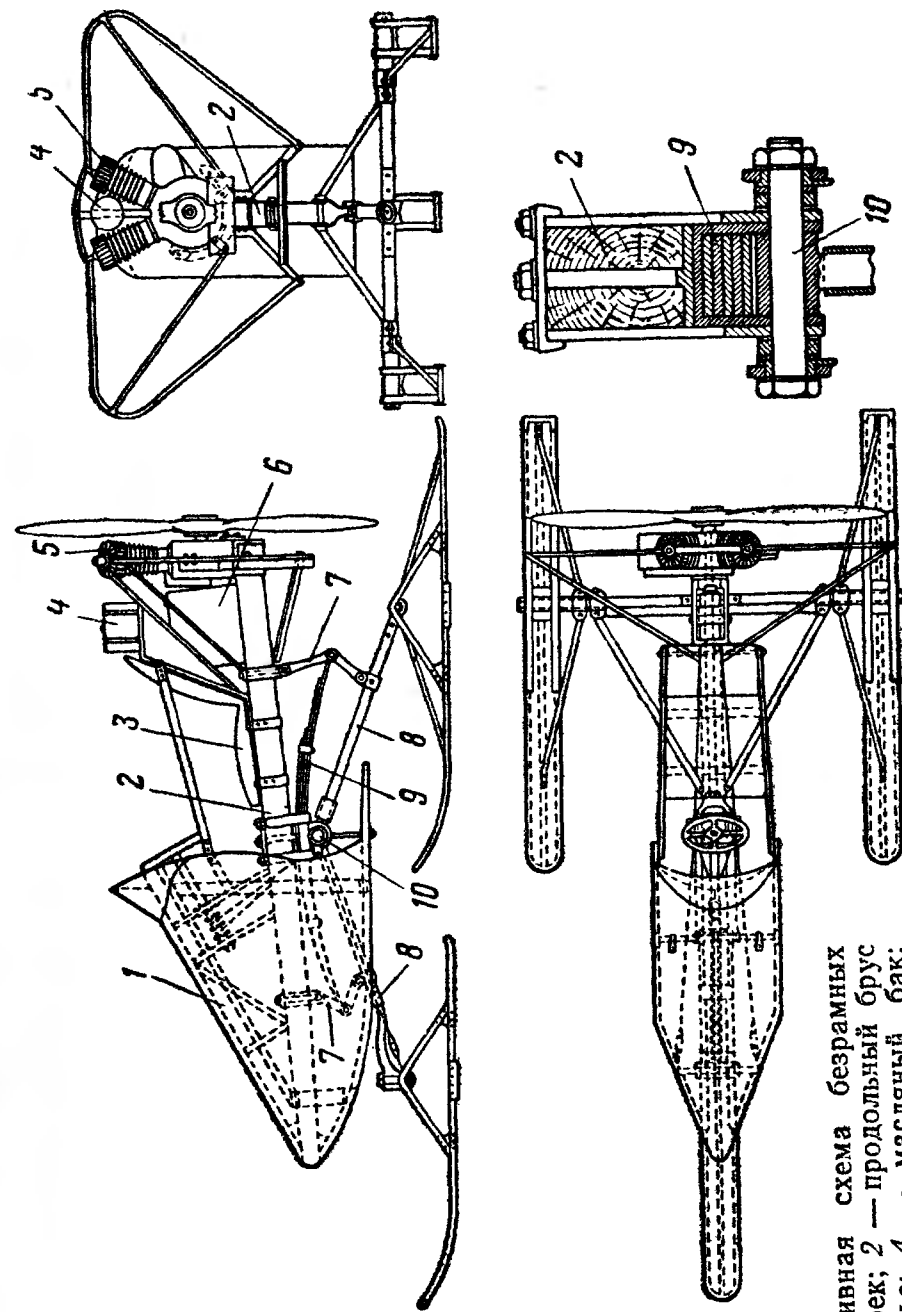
Конструктивная схема безрамных аэросаней: 1 — козырек; 2 — продольный брус корпуса; 3 — сиденье; 4 — масляный бак; 5 — двигатель; 6 — топливный бак; 7 — серья и хомуты; 8 — кронштейн; 9 — рессора; 10 — центральная ось.
